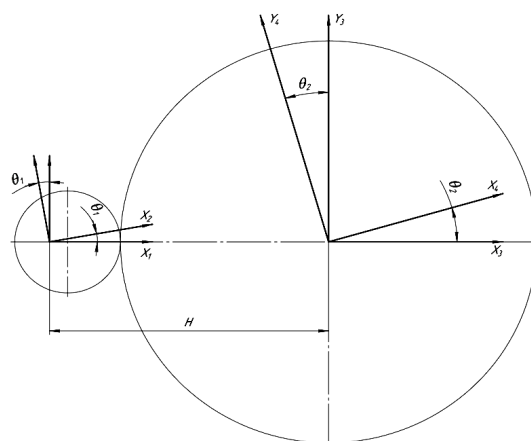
Схема обработки эксцентриковой шейки фрезой-протяжкой
